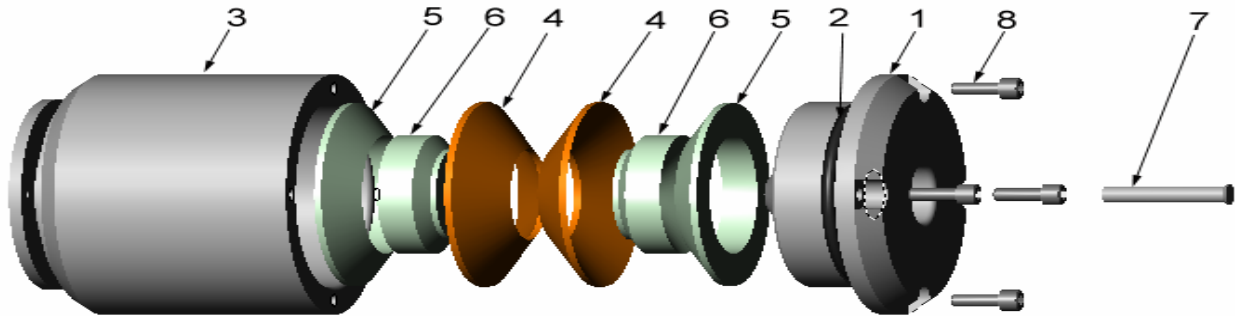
Vue éclatée, dimensions 3,43 po (8,71 cm) -
